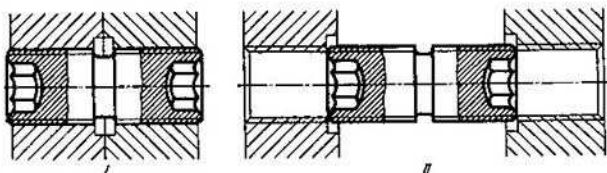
Unión de piezas mediante un tornillo con roscas de direcciones opuestas:
